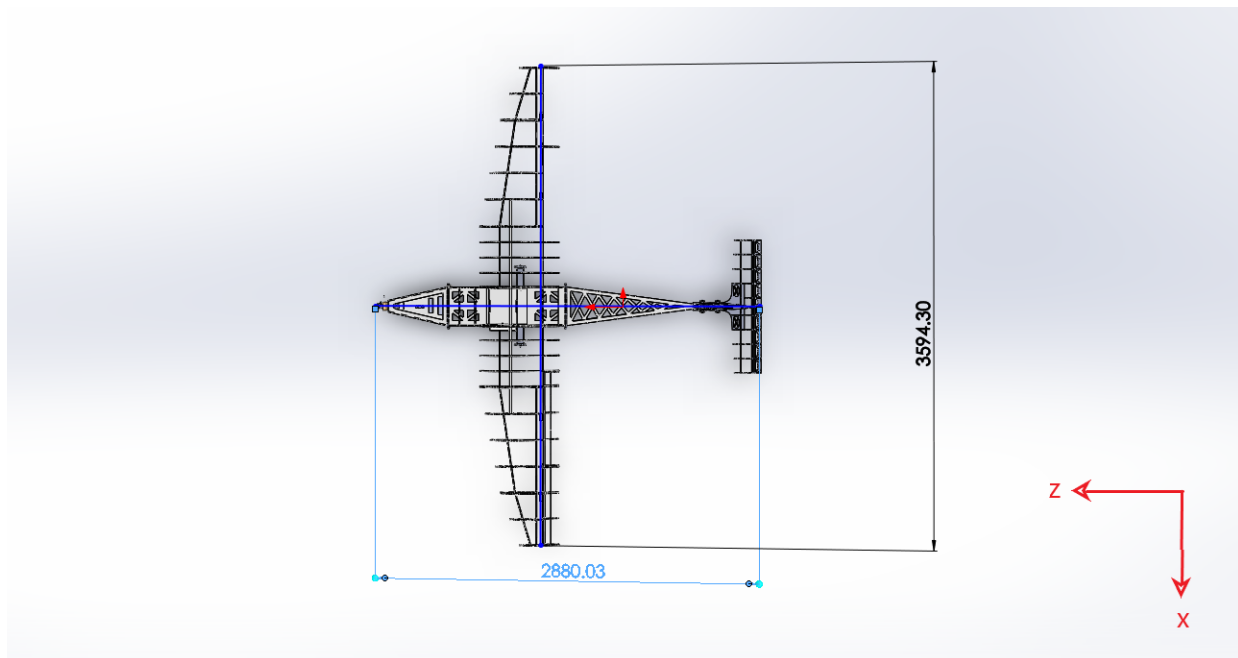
Vista de planta de la estructura (acotaciones en [mm]).
